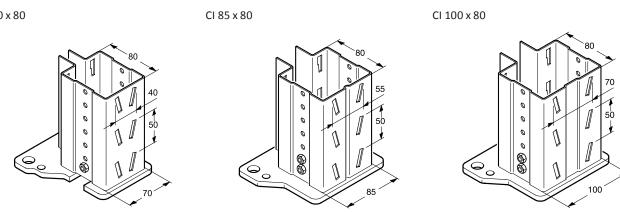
Sections transversales des colonnes des profilés support (dimensions toujours exprimées en mm)
